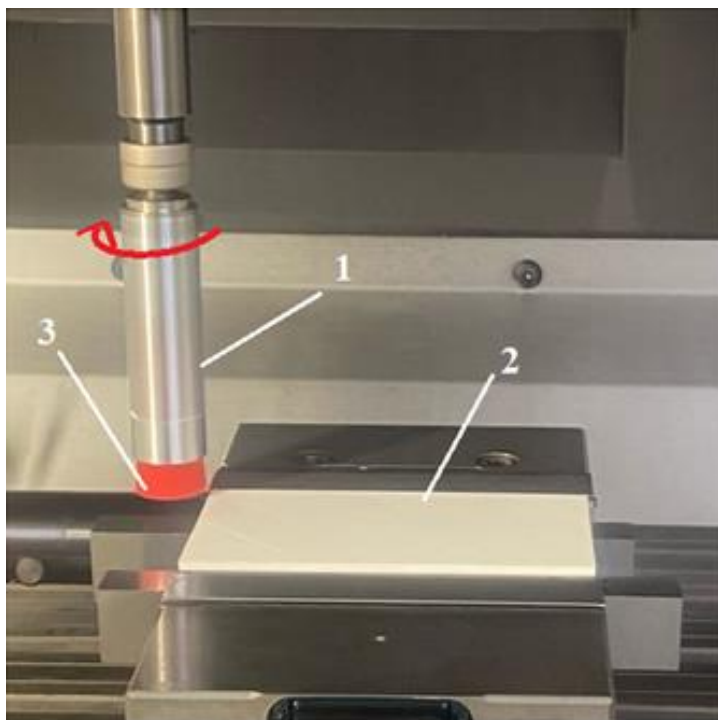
Рабочая область эксперимента 1 — корпус щётки с подаваемой смесью, 2 — обрабатываемая деталь, 3 — гибкий керамический ворс.
